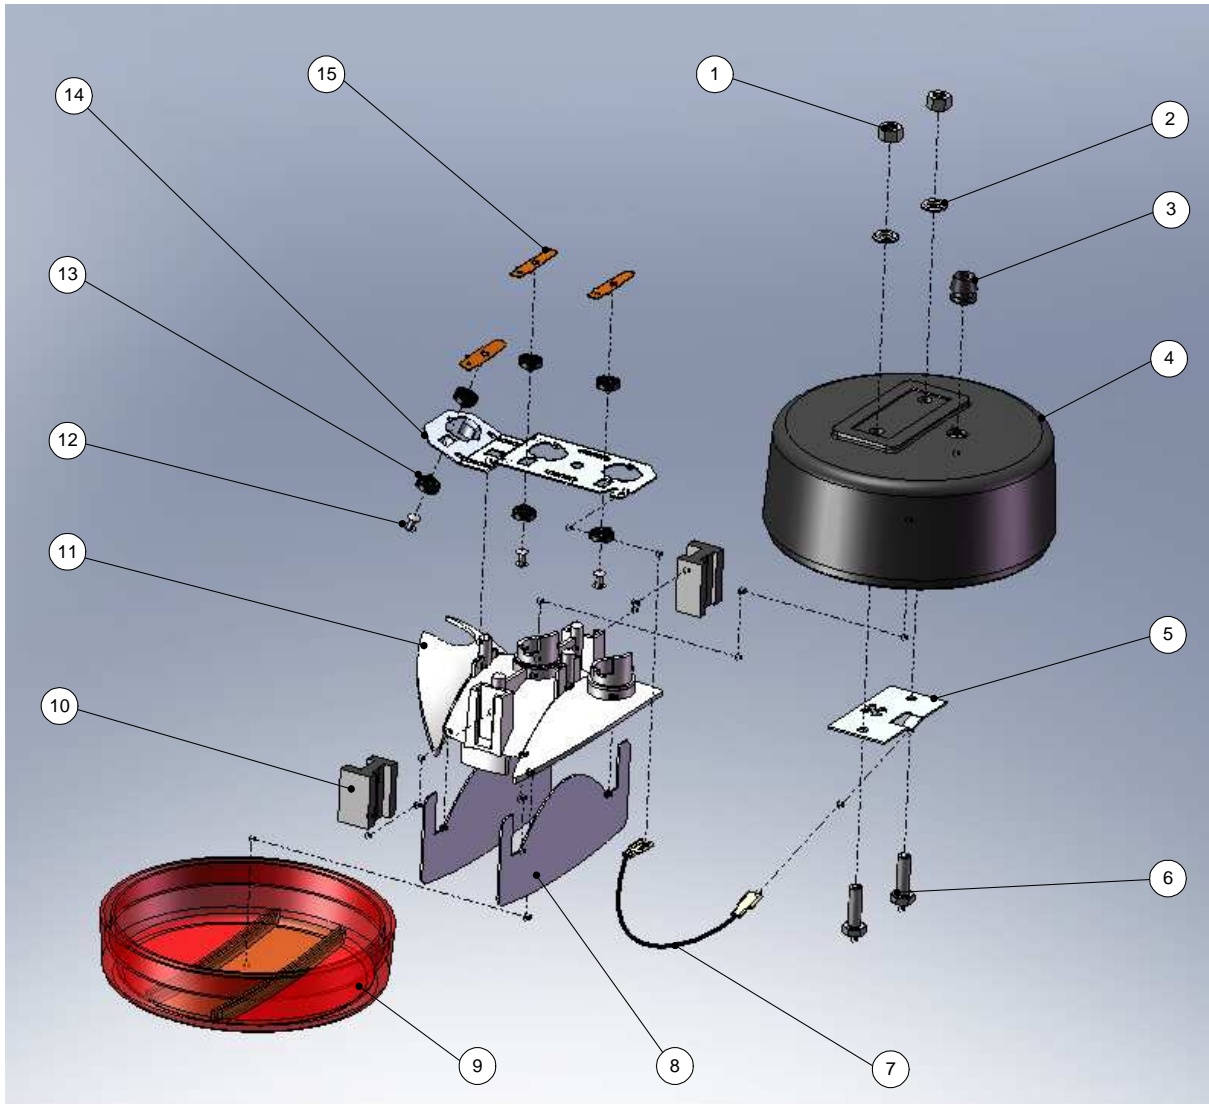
Vista explodida do farolim "Olho de Boi" Original
